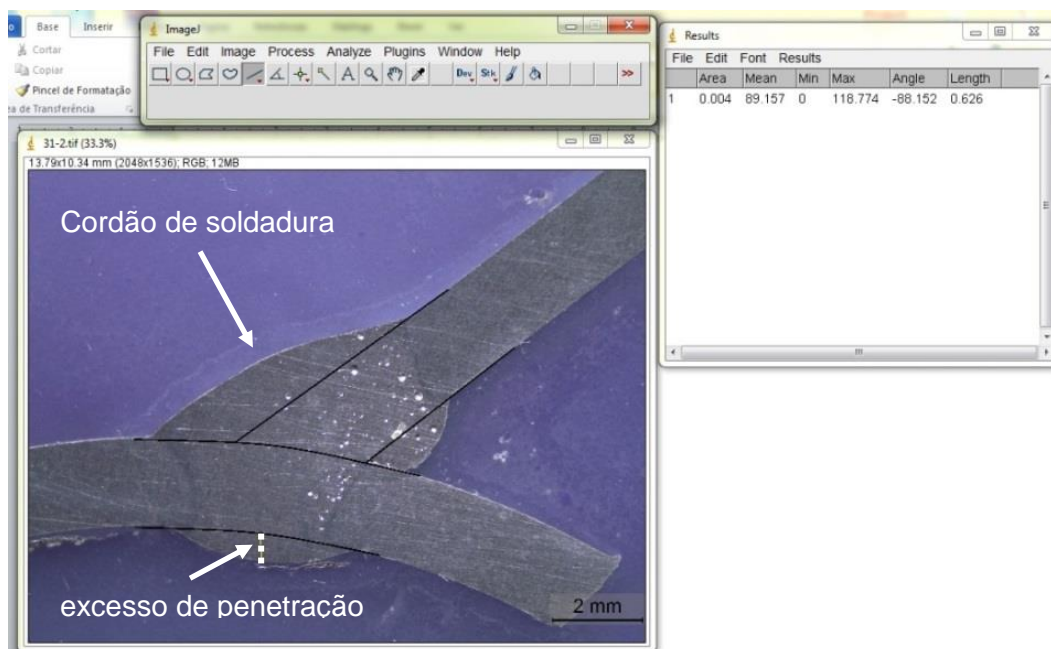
Exemplo de medição do excesso de penetração do cordão de soldadura pelo *software ImageJ*.
